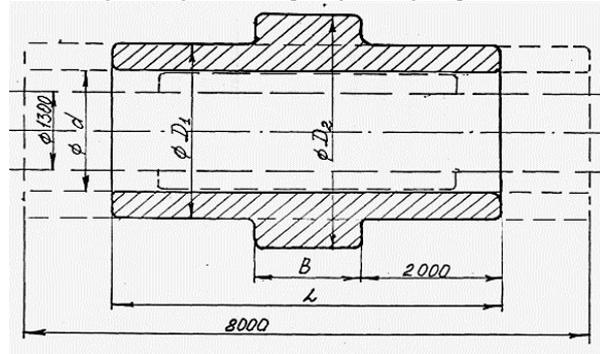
Эскиз ступенчатой трубной поковки для изготовления днищ при различных операциях ковки
